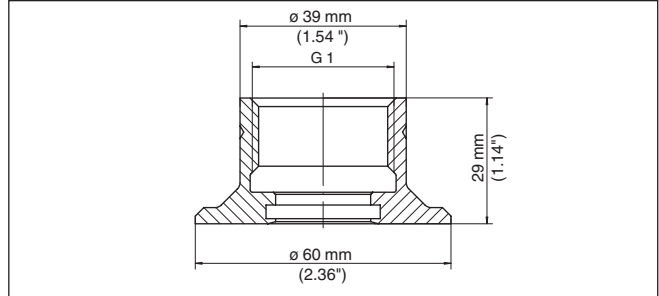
Maße Einschweißstutzen G1 (DIN 3852-X)
